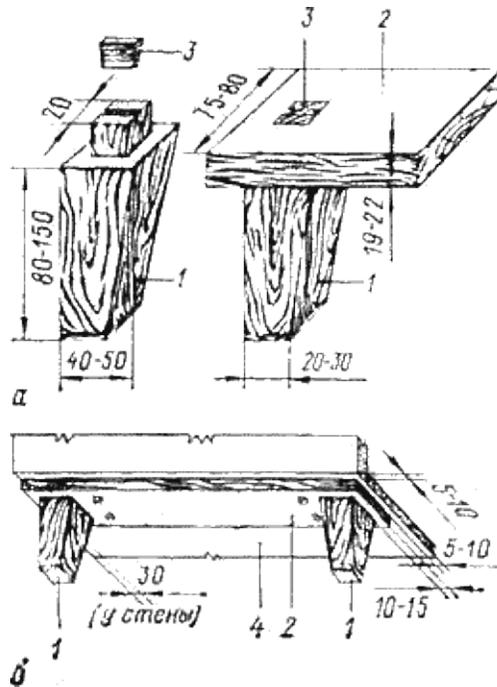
Ножки: а — соединение ножки с накладкой; б — крепление накладки к днищу; 1 — ножка; 2 — накладка; 3 — клин; 4 — днище
